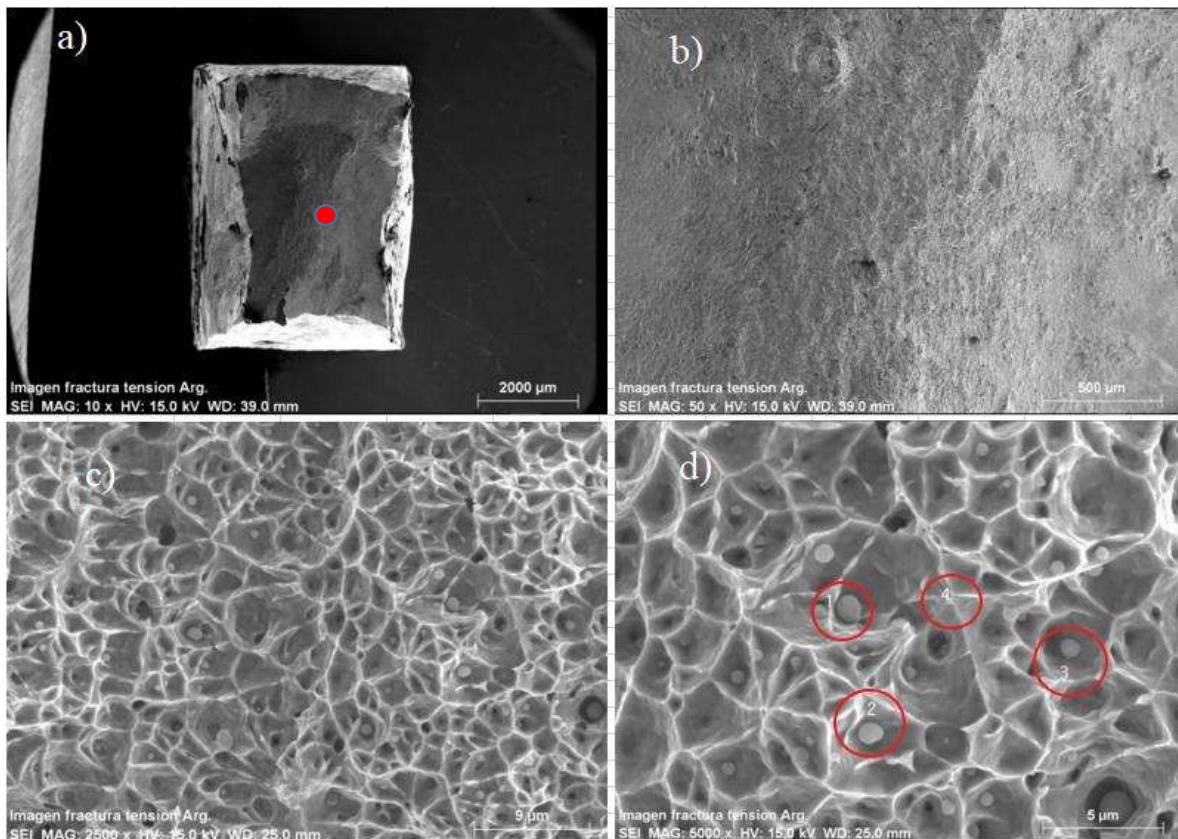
Superficie de fractura de la probeta de tensión soldada con 100% argón.
